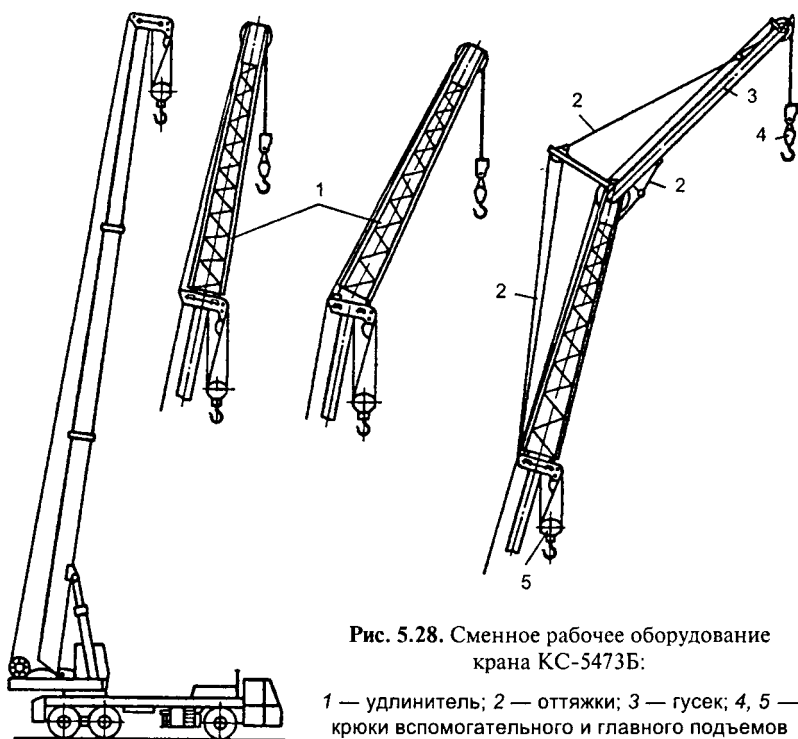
Сменное рабочее оборудование крана КС-5473Б:
